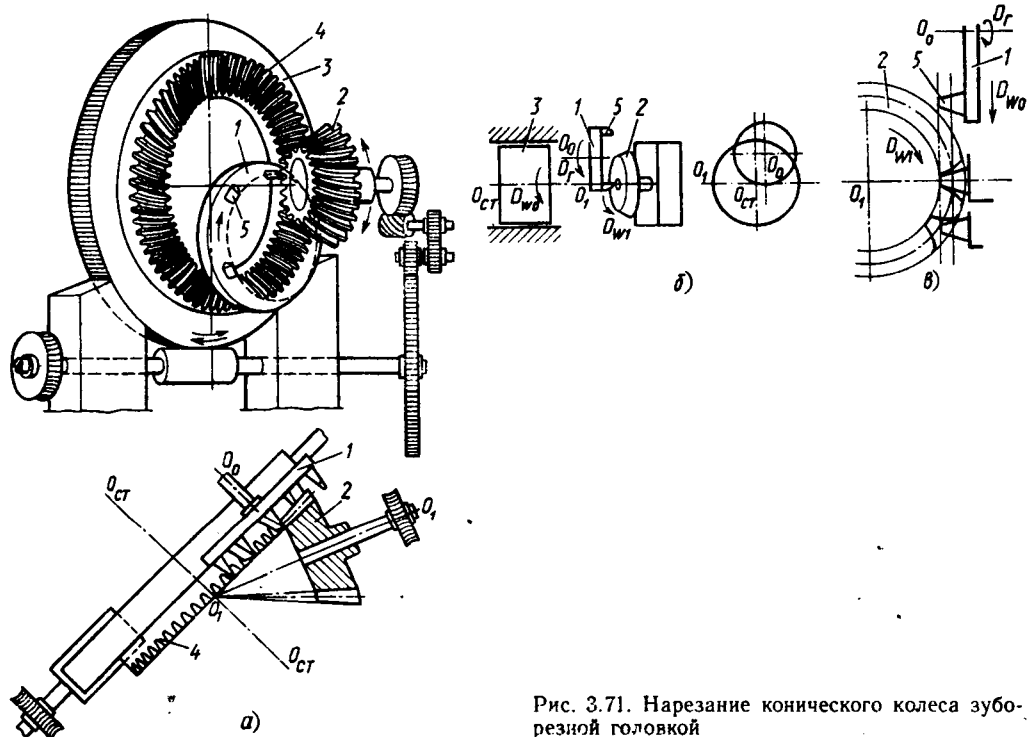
Нарезание конического колеса зуборезной головкой
